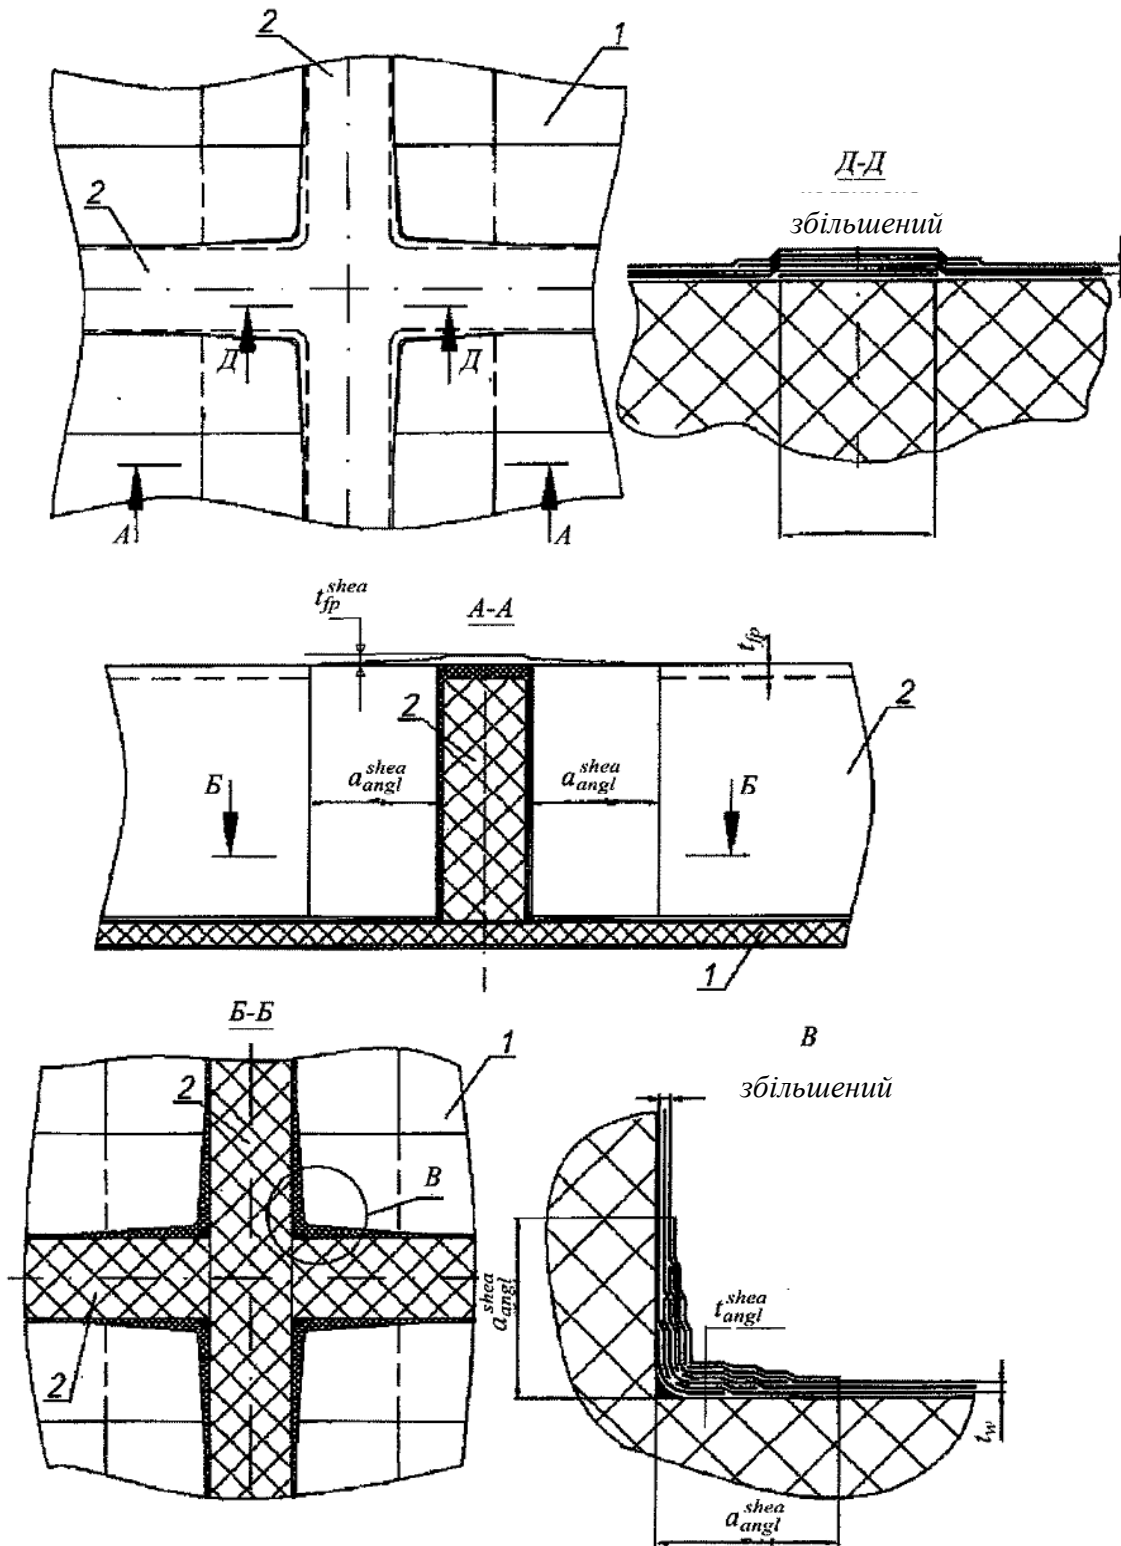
Вузол перетину поздовжньої балки і інтеркостельної поперечної балки, що мають близькі висоти, із забезпеченням безперервності вільних поясків:
